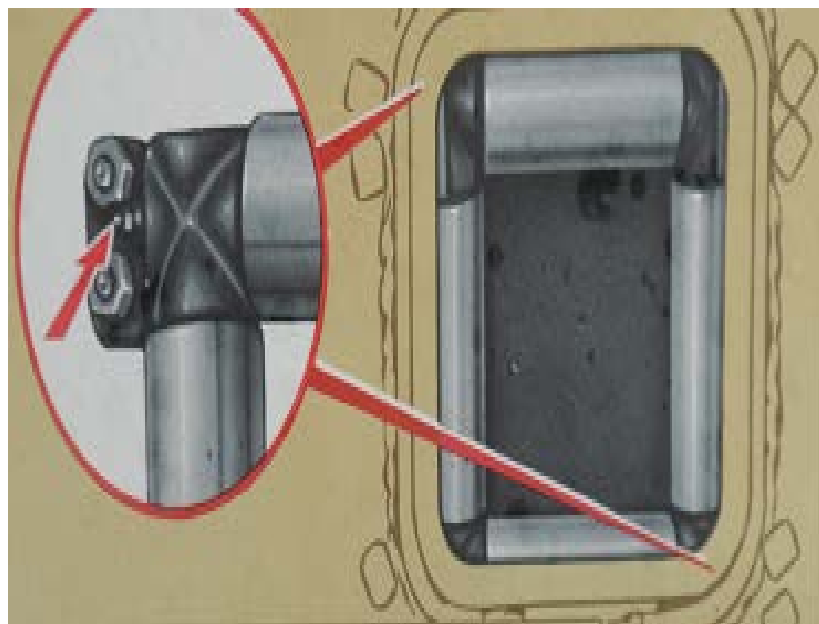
Смазка подшипников направляющих роликов троса лебёдки
